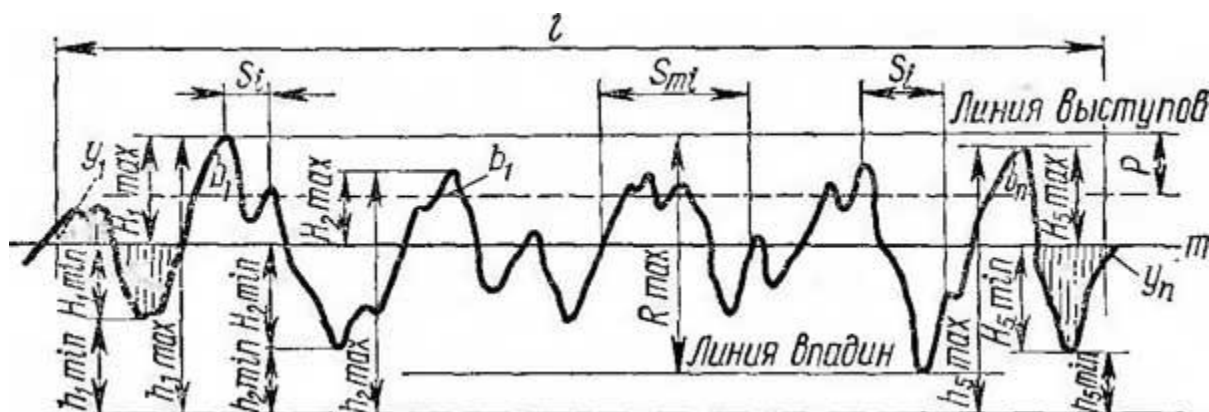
Основные параметры для оценки шероховатости по ГОСТ 2789—73
